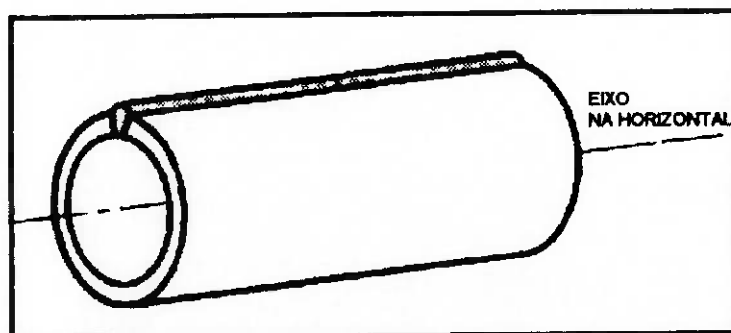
Posição da Soldagem da Junta Longitudinal do Casco Cilíndrico
